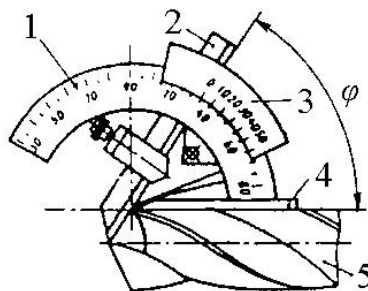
Схема вимірювання половини кута при вершині свердла φ :
